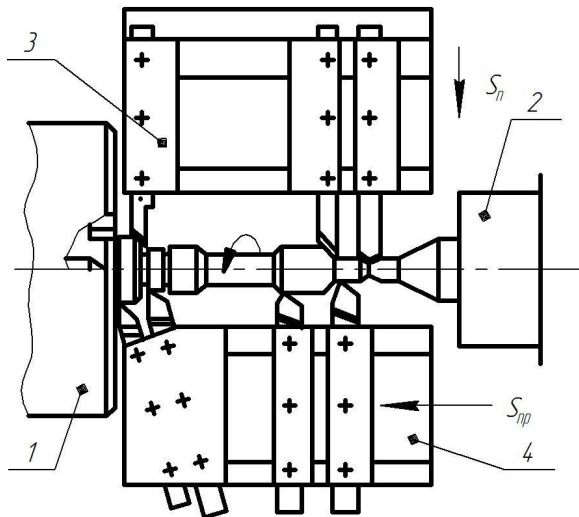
Схема обробки заготовки східчастого валика на токарному багаторізцевому верстаті: 1 – патрон верстата; 2 – задній центр; 3 – поперечний супорт; 4 – поздовжній супорт
